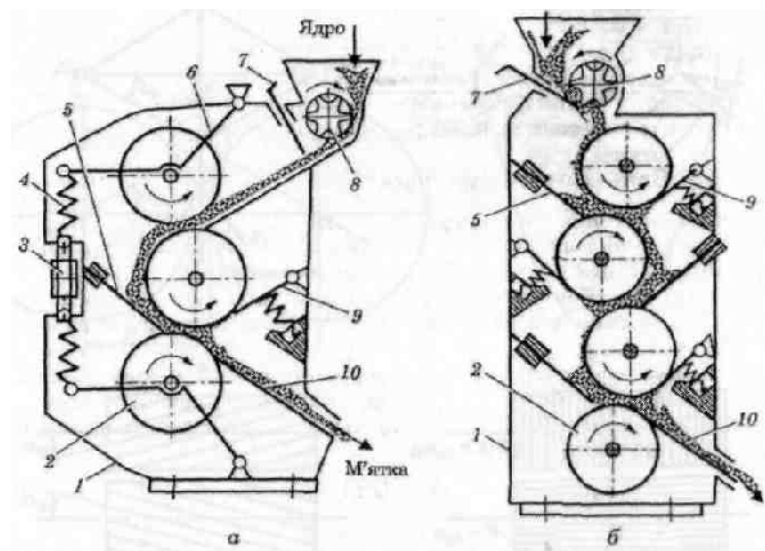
Схеми верстатів для подрібнення насіння олійних культур: *а* – тривальцьового; *б* – чотиривальцьового; 1 – станина; 2 – робочий палець; 3 – пружина; 5 – полиця; 6 – важіль; 7 – заслінка; 8 – живильний валець; 9 – ніж; 10 – лоток.
